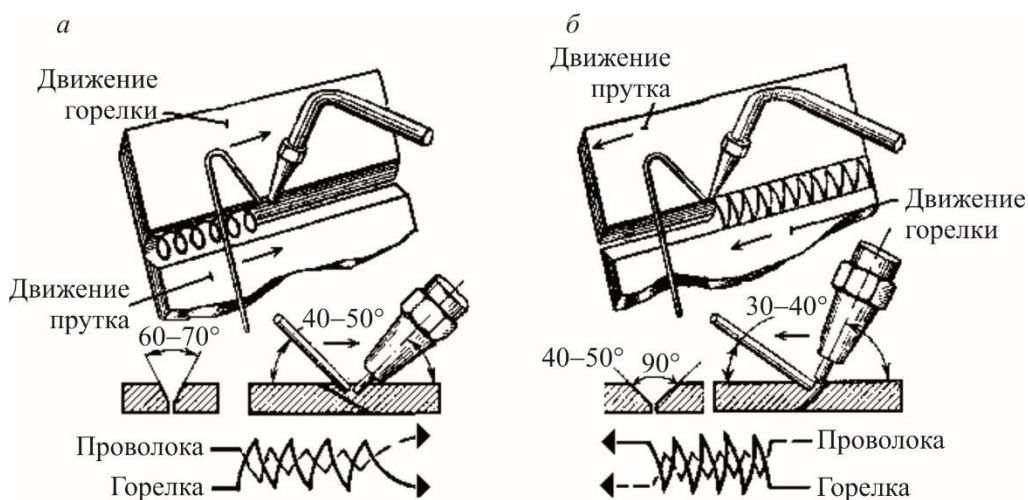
Способы газовой сварки: а – правый; б – левый
